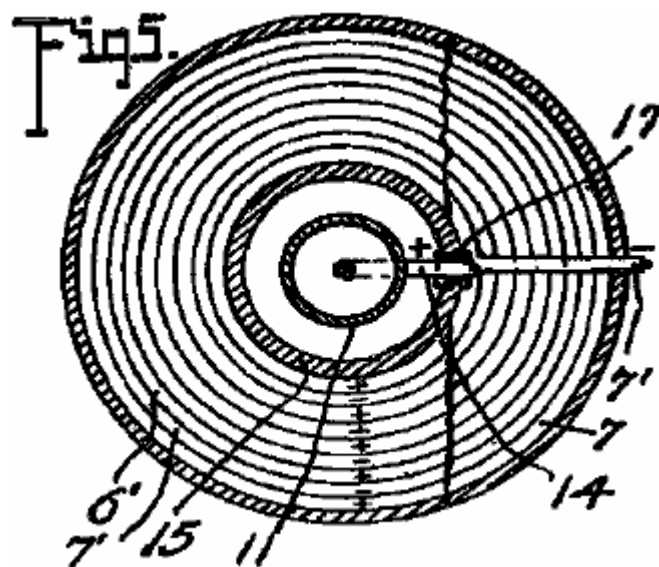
è una sezione trasversale presa sui piani indicati dalla linea 5-5 di Fig. 4, guardando verso il basso.
